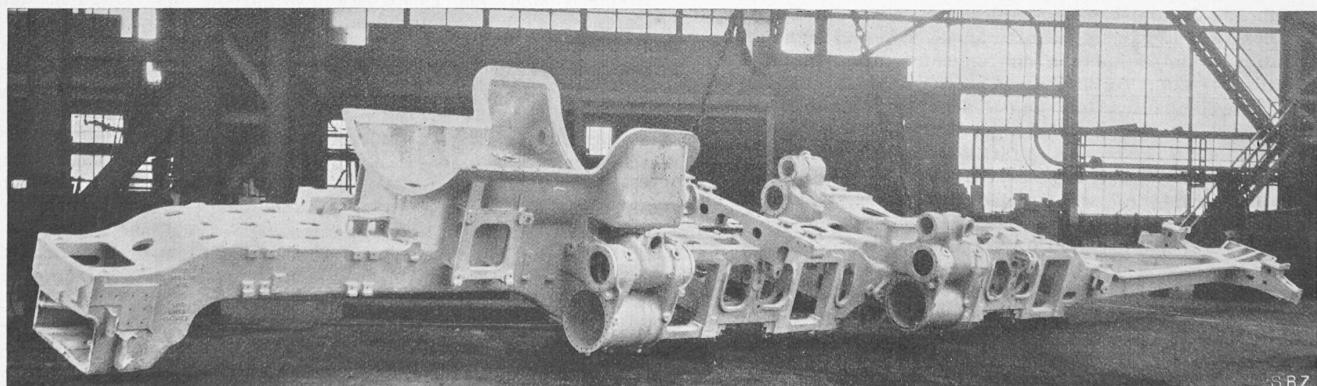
Stahlguss-Unterbau der American Railroads Lokomotive, Klasse S1, Länge des Gusstückes 23,7 m, Gewicht 44,3 t
